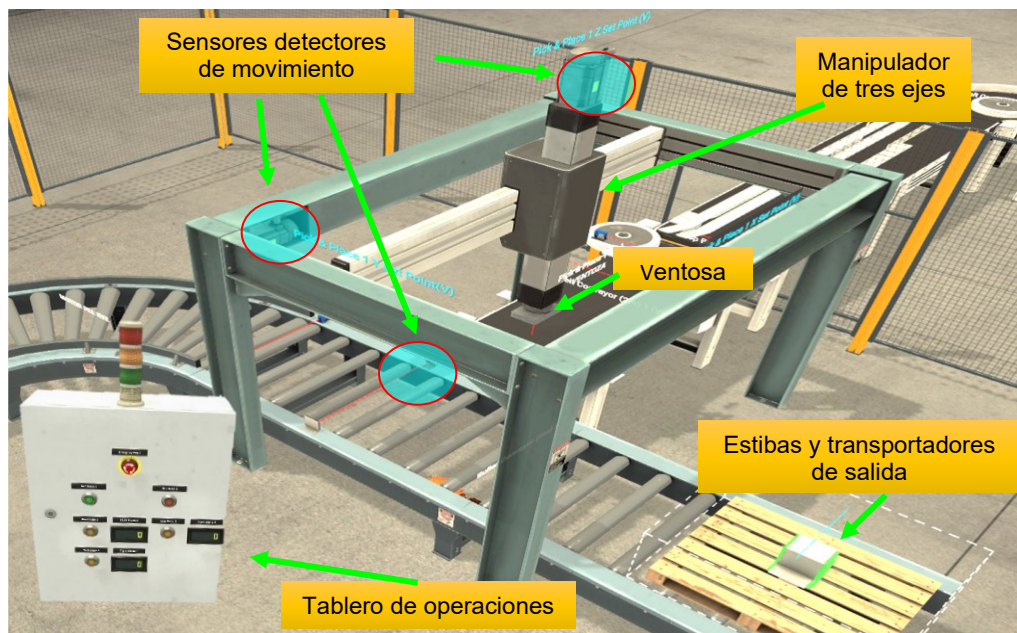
, Componentes estación de trabajo pick and place, elaboración fuente propia.
